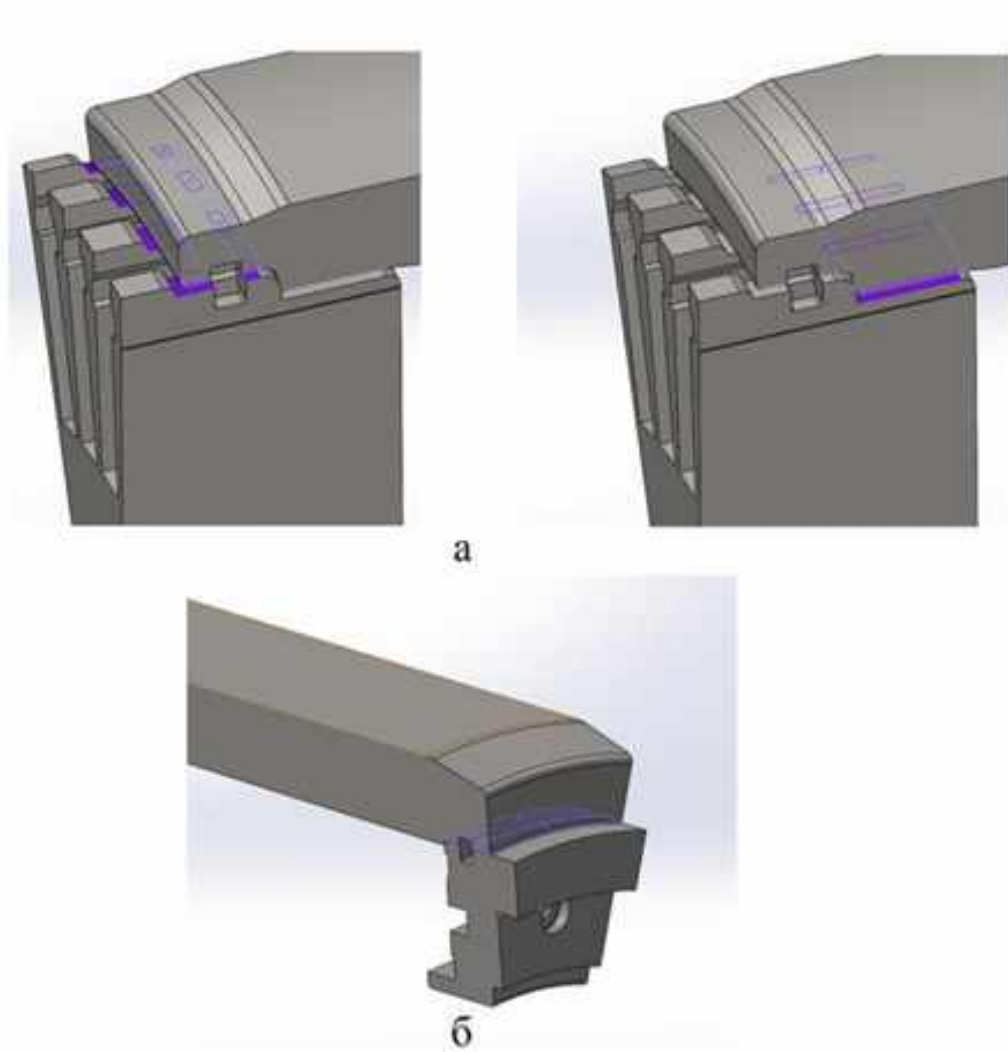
Поверхні з натягом: а – бочка ротора та бандажне кільце;
